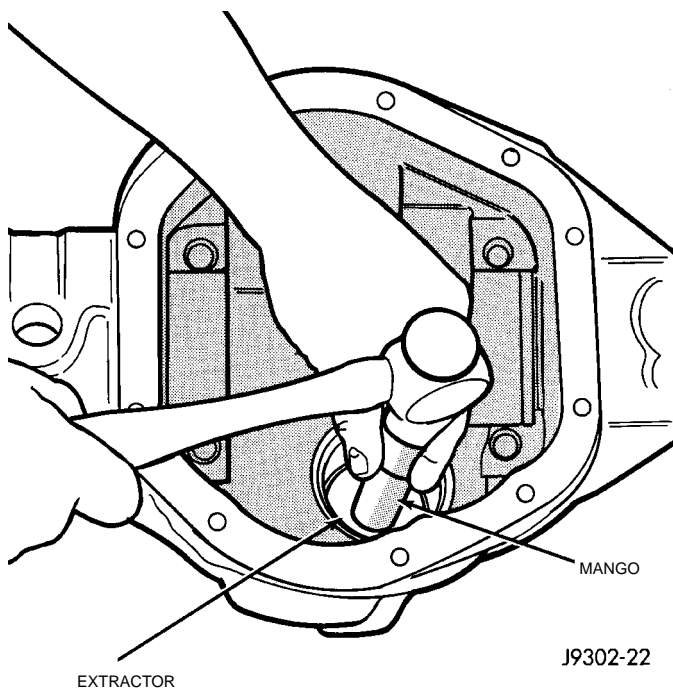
Desmontaje de la cubeta del cojinete delantero
